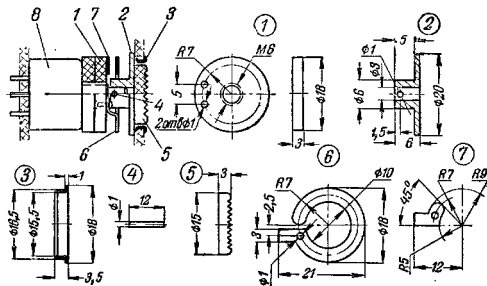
Конструкция выключателя питания и размеры его деталей.
